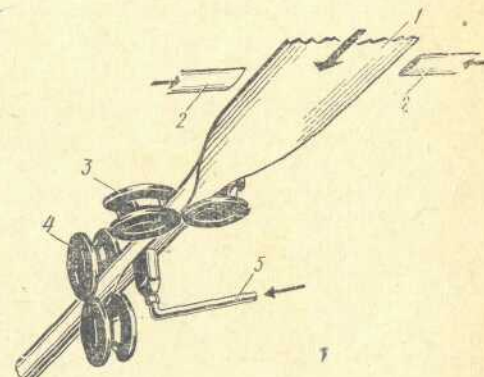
Схема процесса непрерывной печной сварки труб встык
